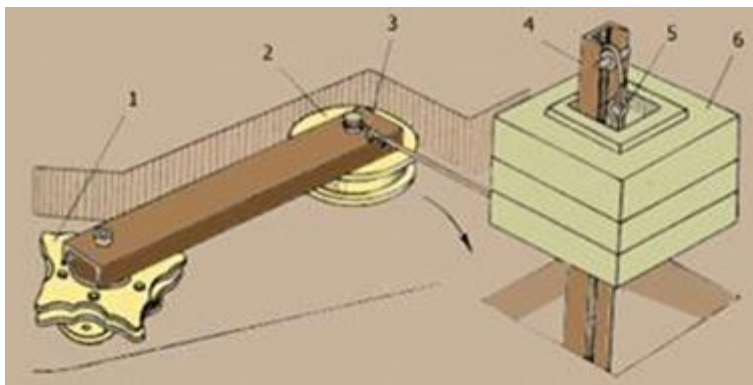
Автоматичний натяжний пристрій конвеєра КСГ-7: 1 – поворотна зірочка; 2 – натяжний ролик; 3 – важель натяжного ролика; 4 – стояк вантажу; 5 – трос підвішування вантажу; 6 – вантаж
